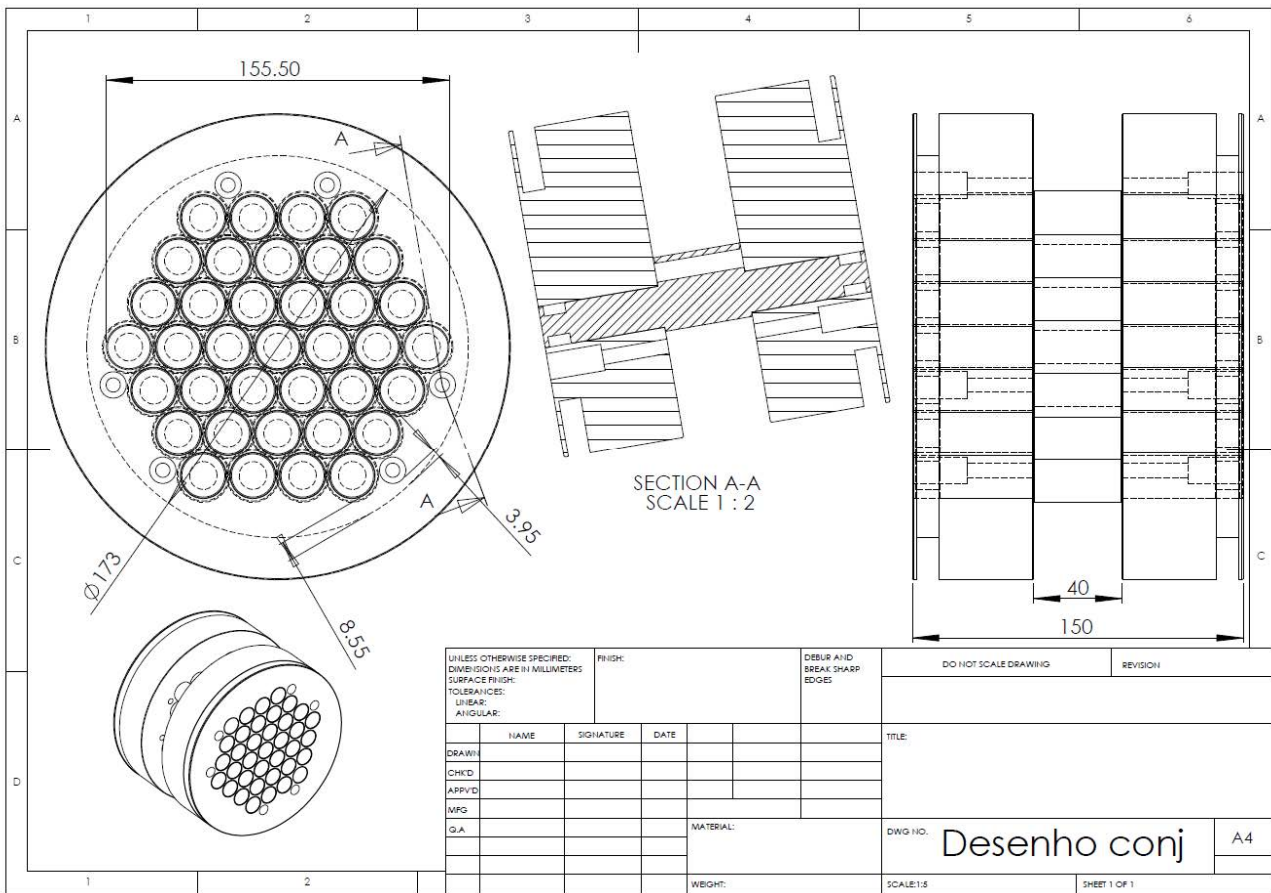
Desenho técnico conjunto do sistema BAC planar 3.
